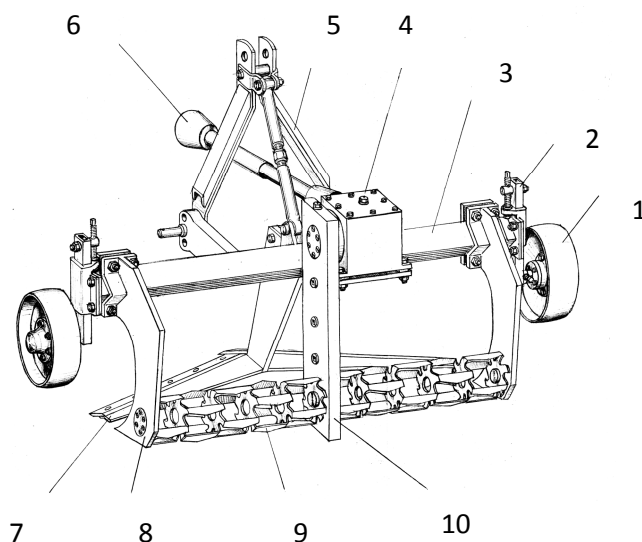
Схема комбинированного подпокровного фрезерователя:
